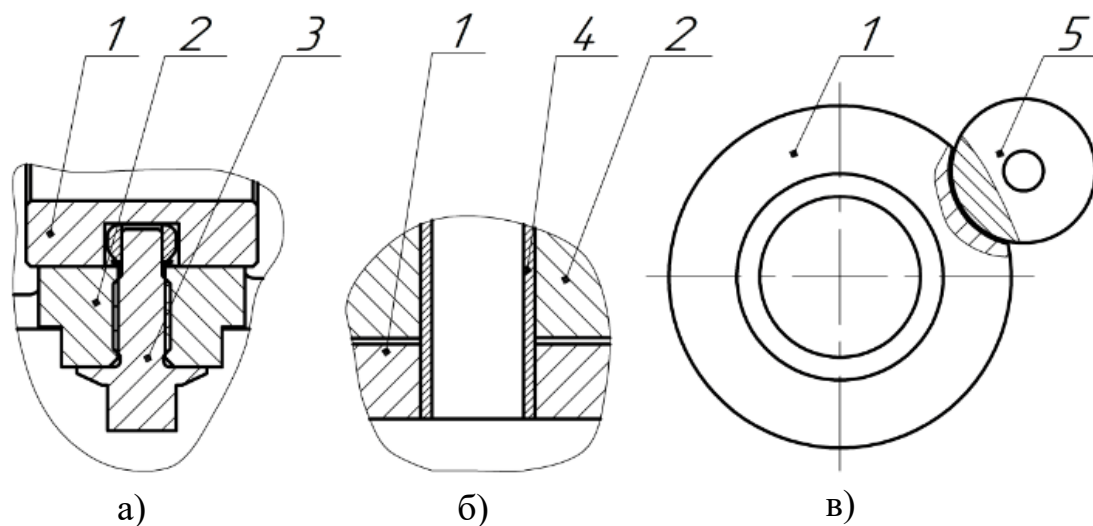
Конструктивные способы предотвращения вращения у ПН втулок: а) Болтовое крепление; б) штифтовое крепление; в) крепление с помощью фиксатора; 1 – ПН втулка; 2 – корпус подшипников; 3 – болт; 4 – штифт; 5 – фиксатор
